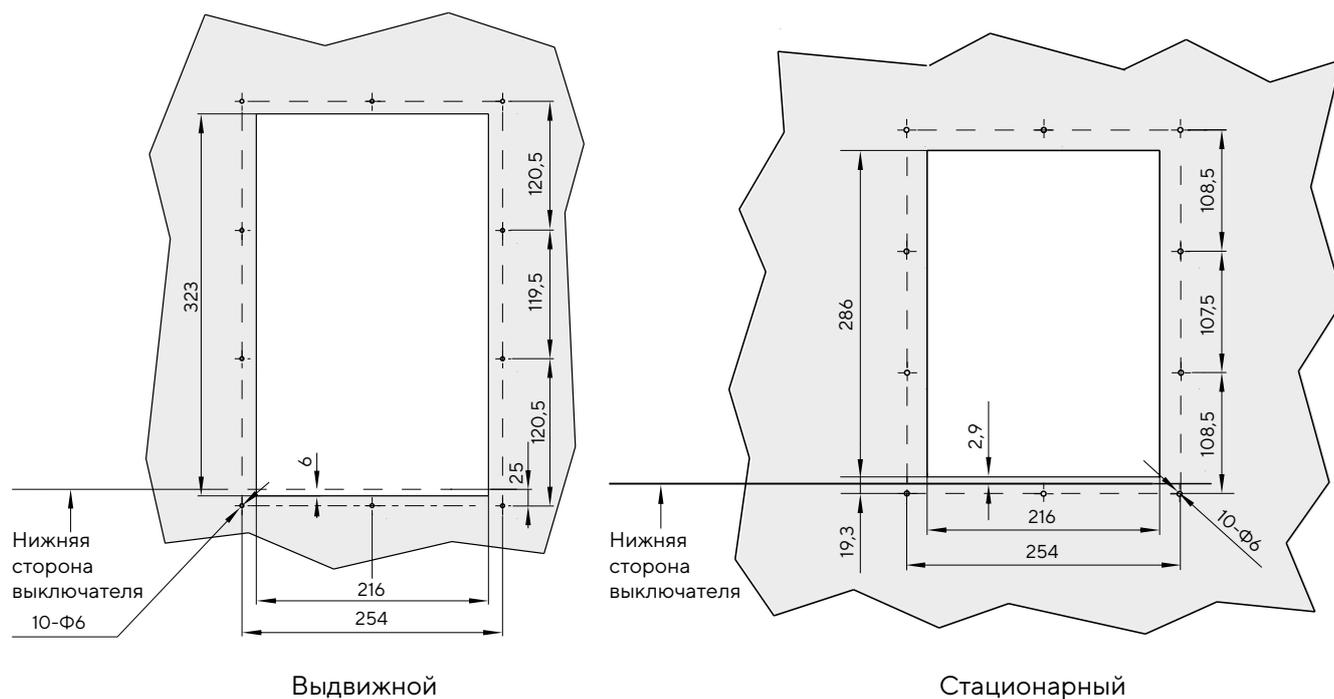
Габаритные размеры рамки обрамления выреза в двери для выключателей типоразмера А
